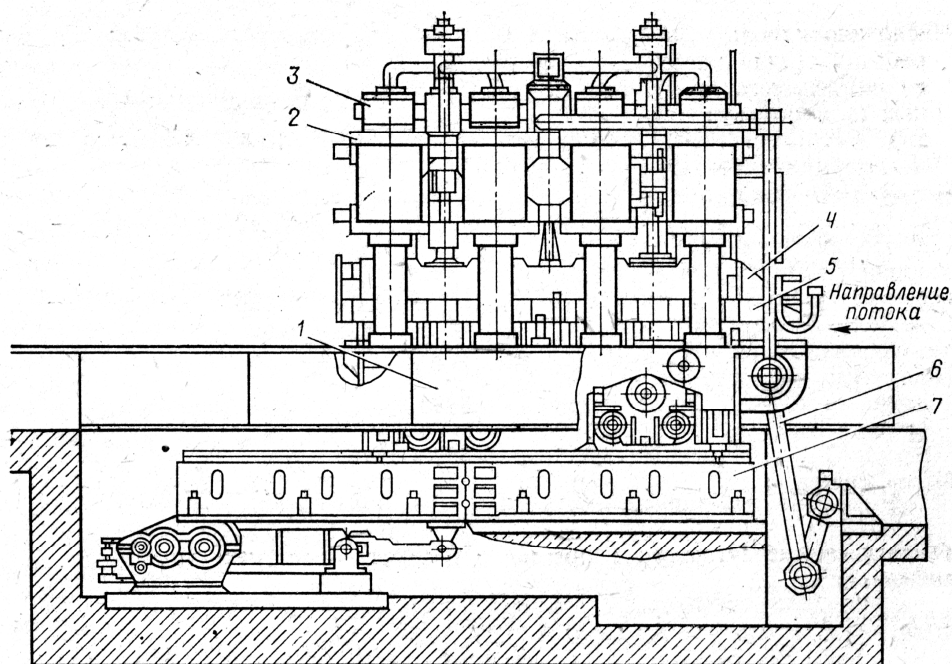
Шагающий пресс с возвратно-поступательным движением:
